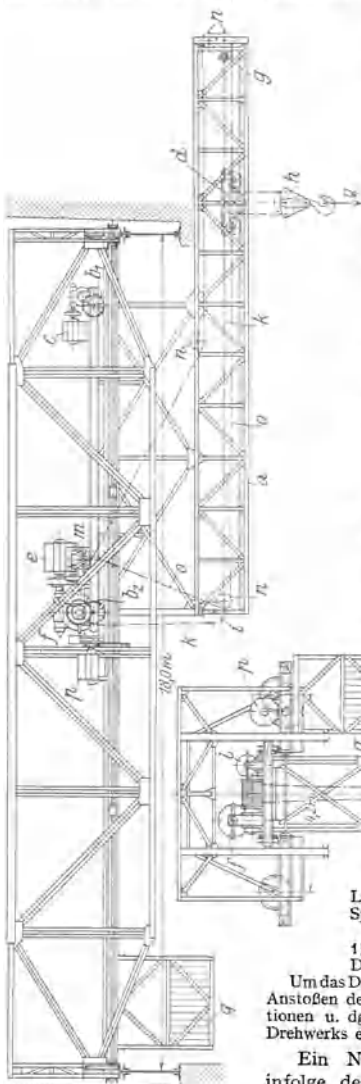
Laufkran mit verschiebbarem Ausleger. a verschiebbarer Ausleger; b_1 - b_2 Laufrollenpaar; c Ausleger-Fahrmotor; d Laufkatze; e Hubmotor; f Trommel; g Ausleger-Fahrmotor; h Kranflasche; i Umlenkrollen; k Seilzug zum Hubwerk; j Katzenfahrmotor; m Trommel; n Umlenkrollen; o Seilzug zum Katzentfahrwerk; p Kranfahrmotor; q Führerkorb.
